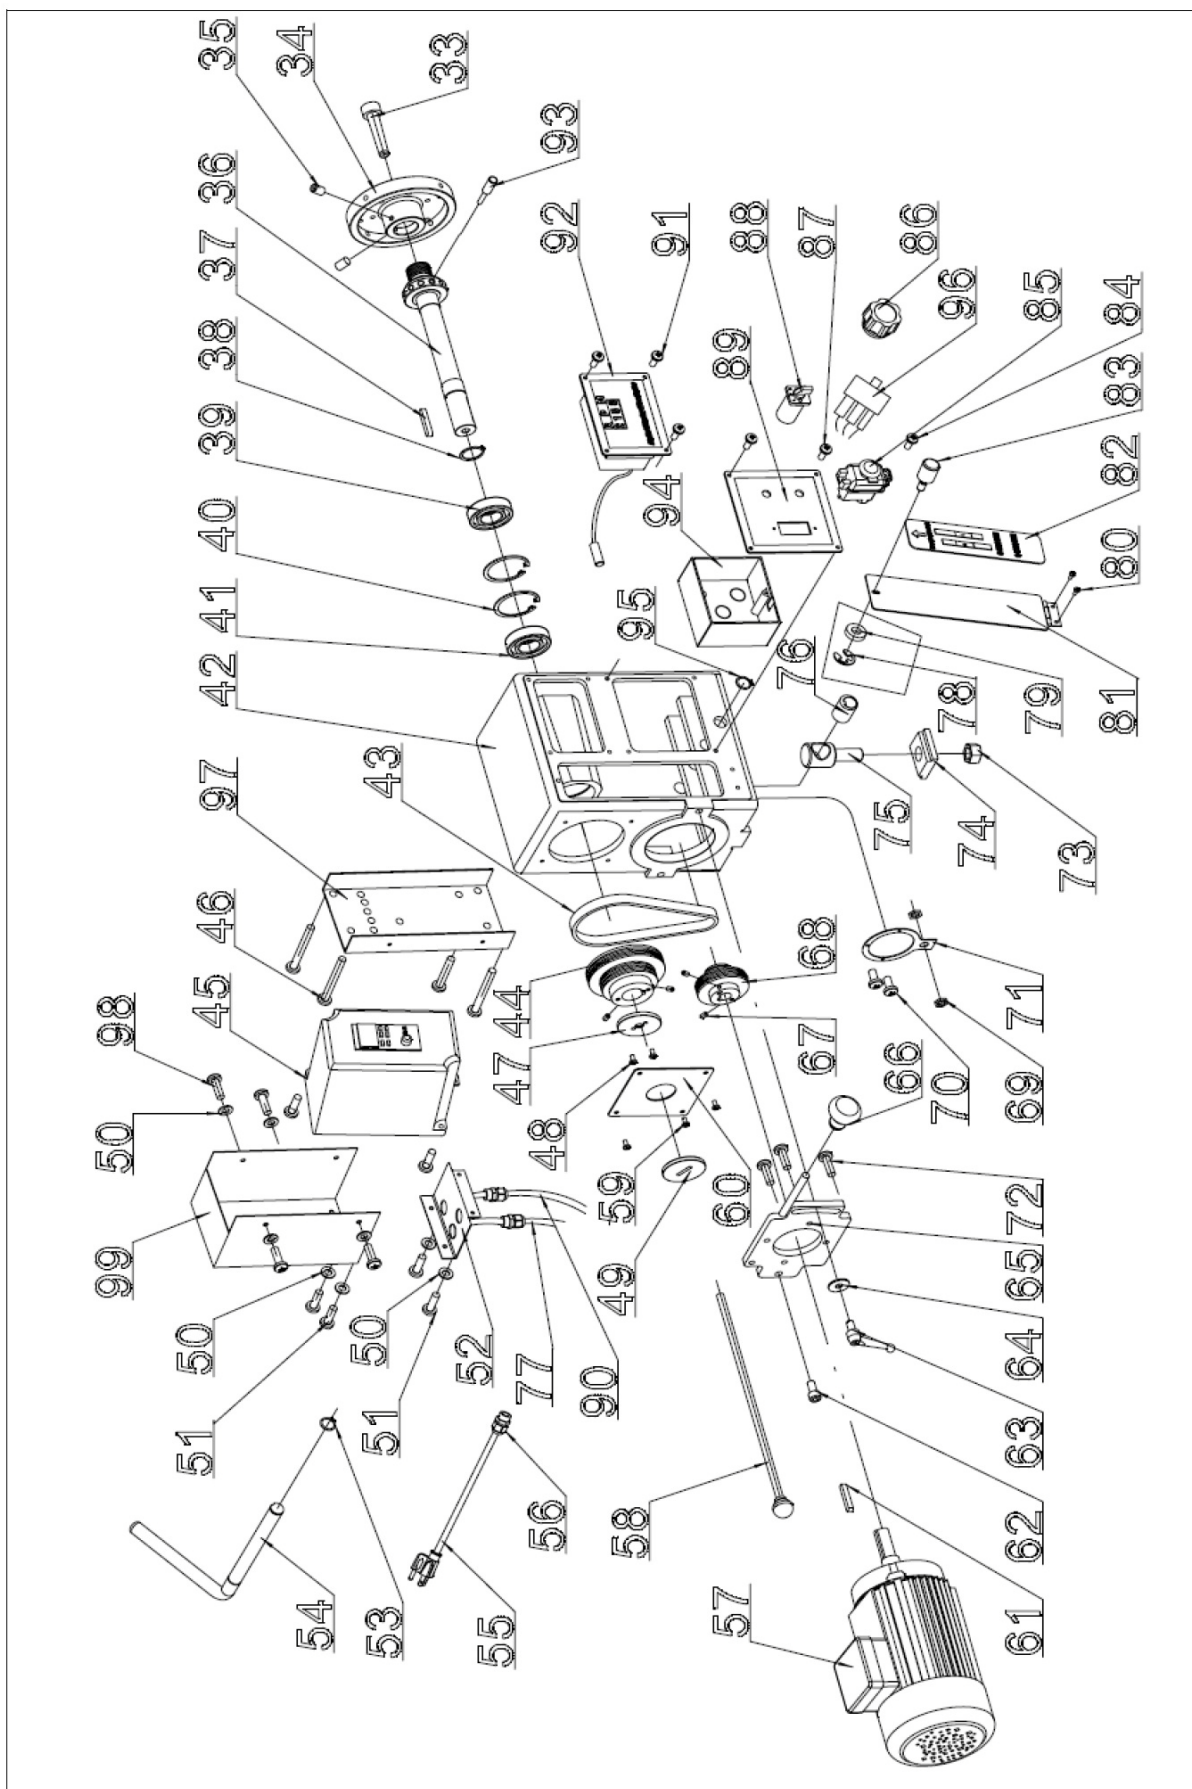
Схематический чертеж 2 Токарный станок по дереву DB 1202
